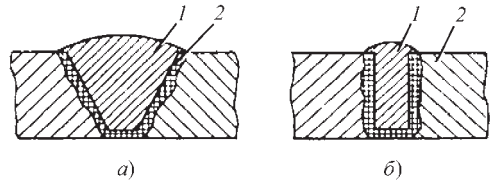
Поперечное сечение шва при сварке с V-образной (а) и щелевой (б) разделкой: 1 — наплавленный металл; 2 — основной металл
